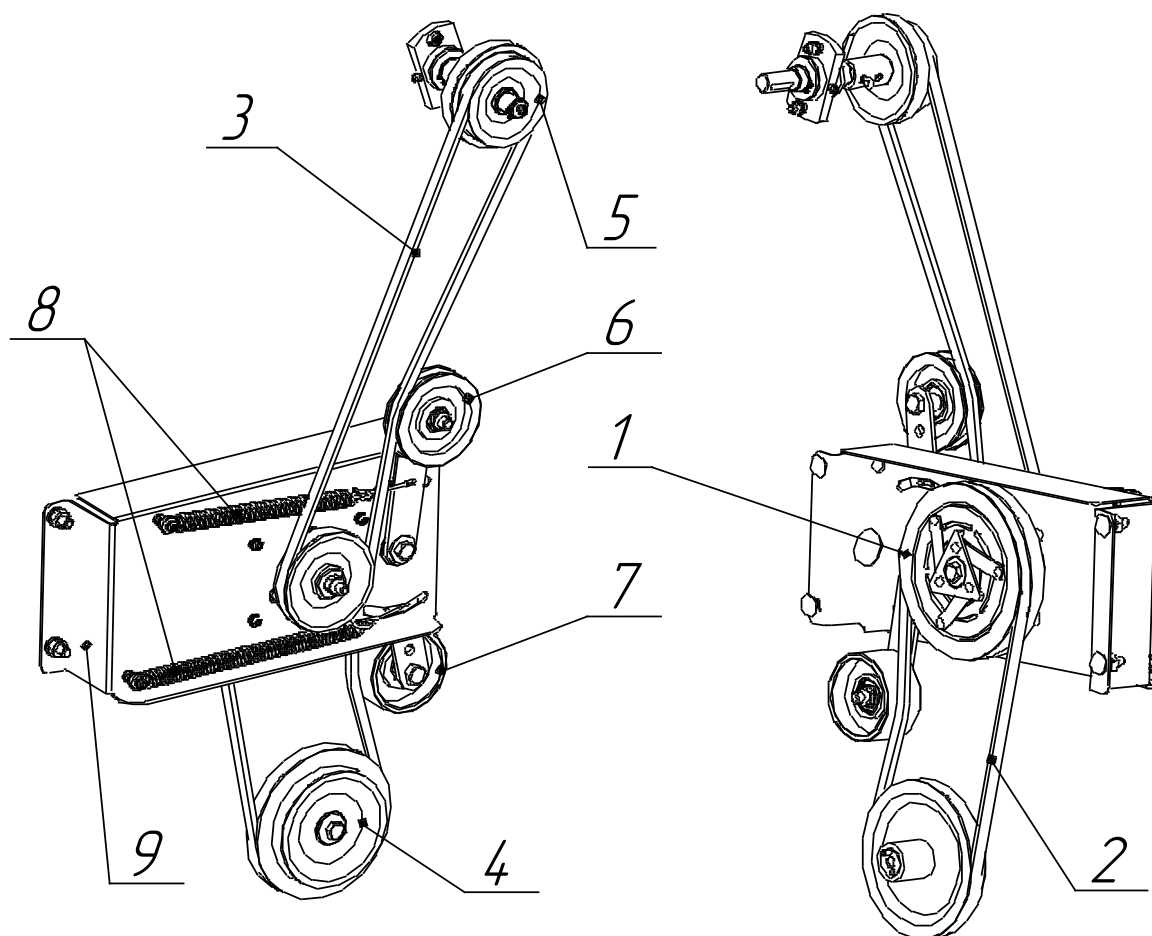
Механизм привода обвязки: 1 – электромуфта; 2 – ремень привода электромуфты; 3 – ремень привода механизма обвязки; 4 – шкив привода электромуфты; 5 – шкив привода механизма обвязки; 6 – натяжной ролик; 7 – натяжной ролик; 8 – пружина натяжного ролика; 9 – корпус электромуфты.
